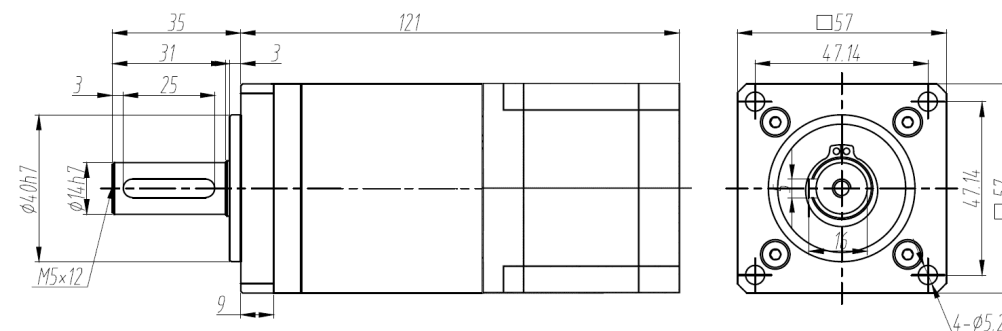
Габаритные и присоединительные размеры ШДР57-2,8-9-1/5
